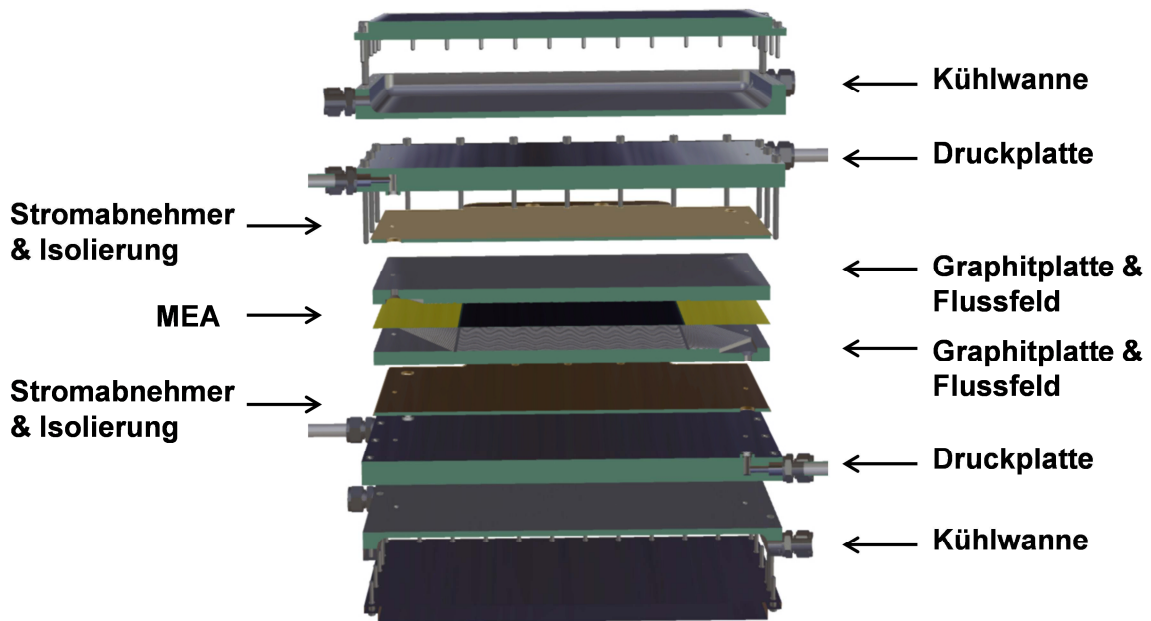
Aufbau Laboreinzelzelle, Explosionszeichnung
